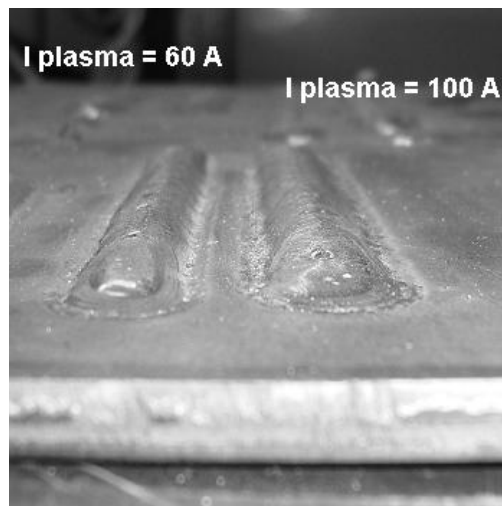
Comparação entre a largura do cordão das soldas do teste 1 e teste 2
